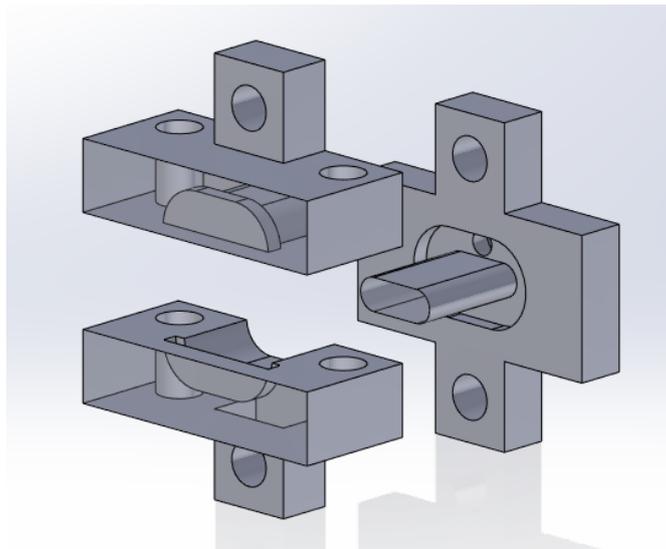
Molde de injeção da peça a inserir no suporte do travão
